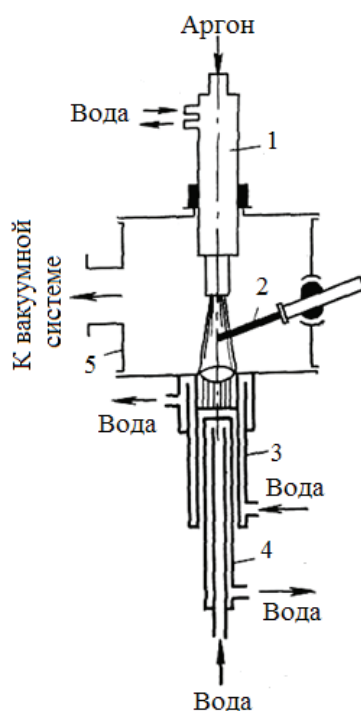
Схема плазменной установки с вытягиванием слитка из кристаллизатора:
